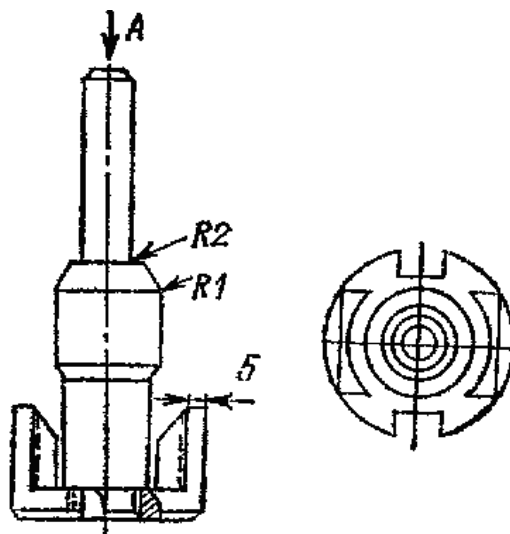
Пристрій для запресування статора в електродвигун натирача
